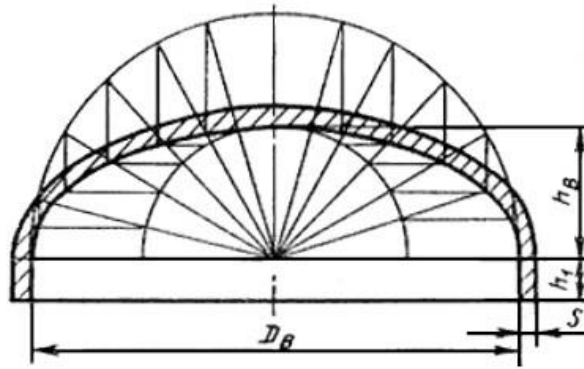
основные размеры днищ с внутренними базовыми размерами [9]
